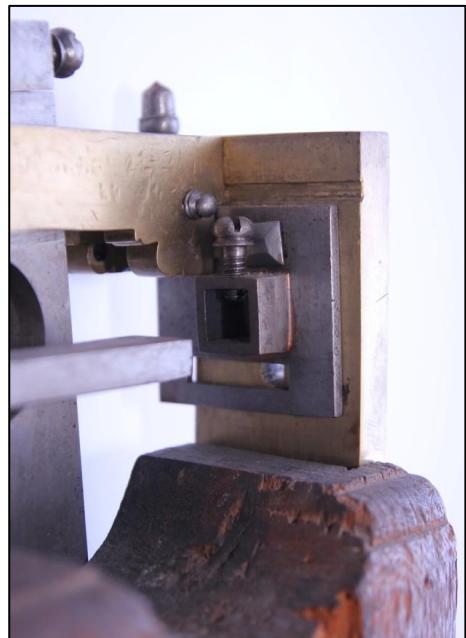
Spindeldok nr. 3952 med holder til aftasteren (detalje)
